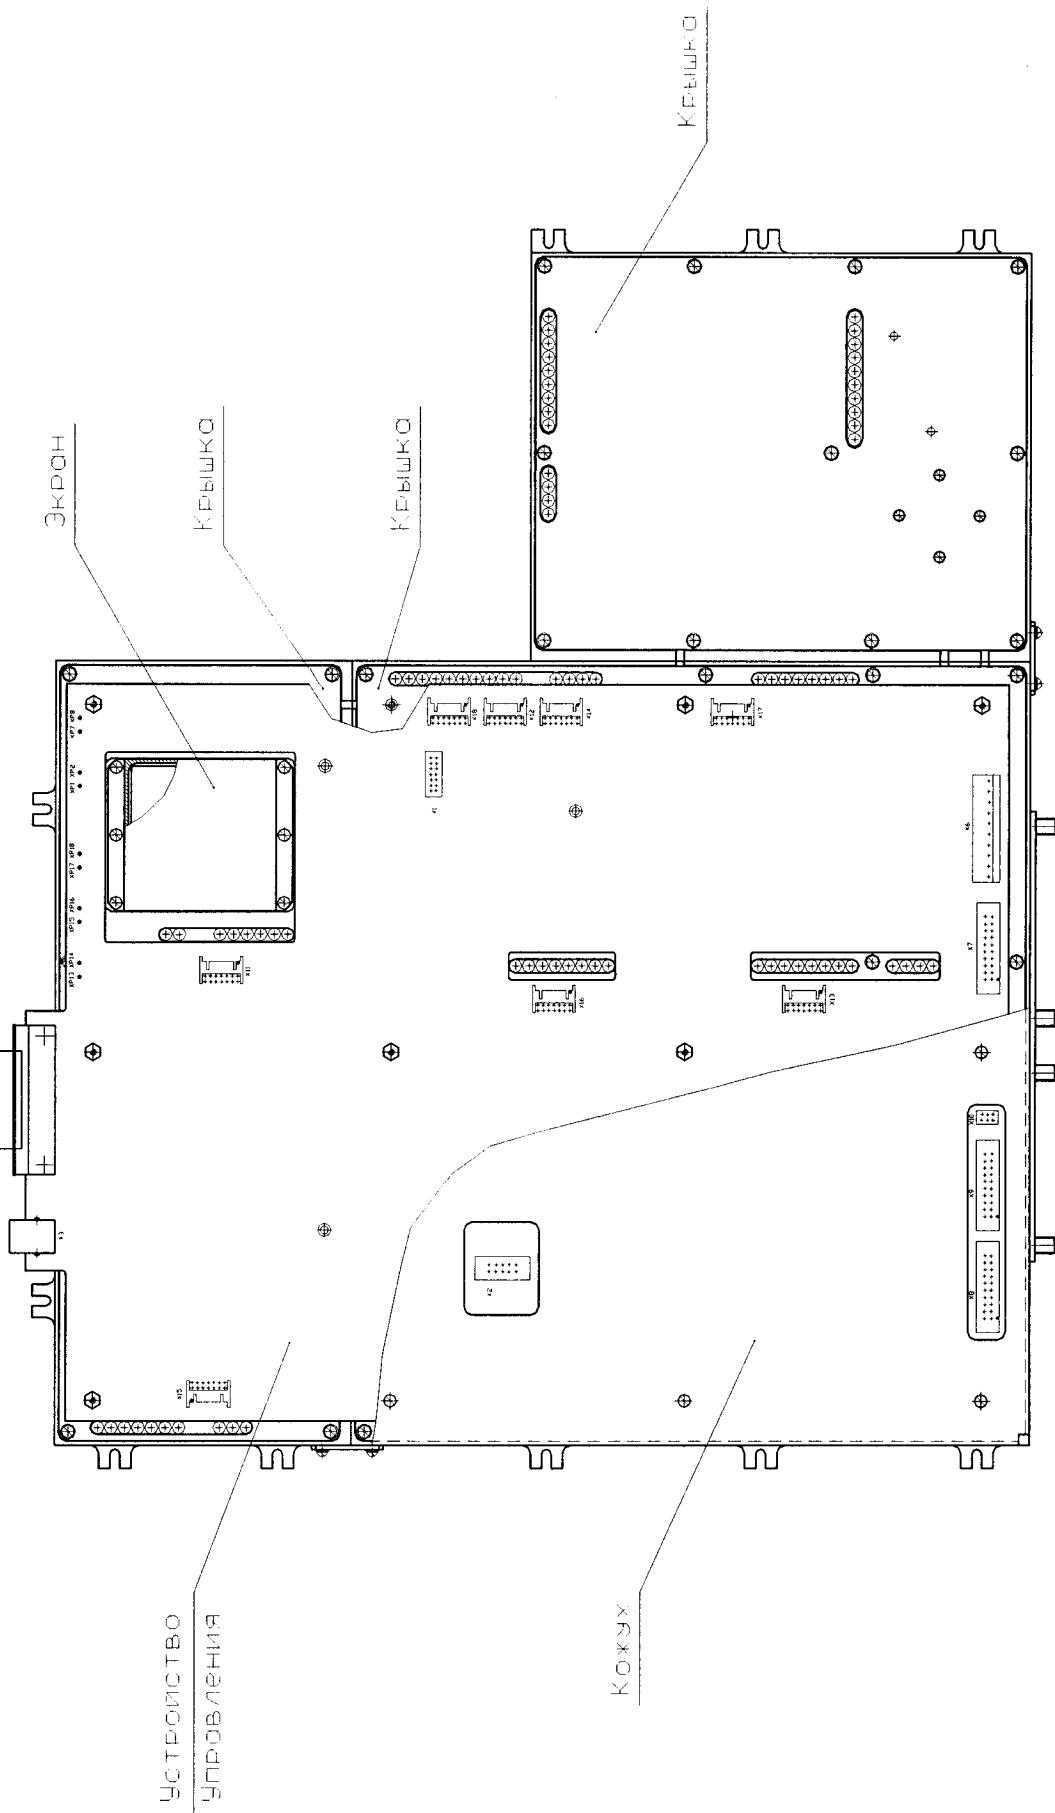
Конструкция блока комбинированного ТНСК.468128.001, вид снизу
